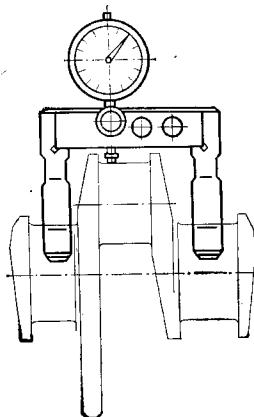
Приспособление для измерения радиуса кривошипа коленчатого вала
